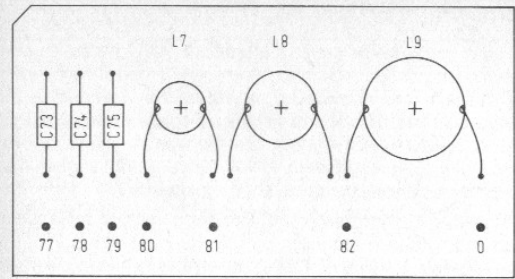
Plan d'implantation du filtre de dérivation III.
